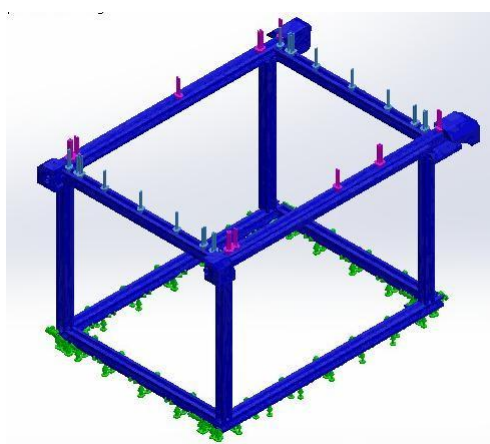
Disposición de cargas aplicadas a la estructura.
